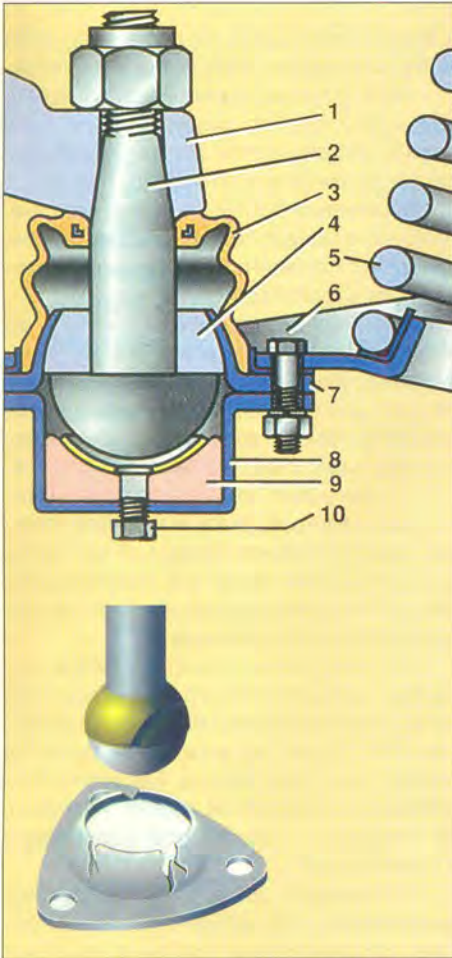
Изношенная нижняя опора: 1 – поворотный кулак; 2 – шаровой палец; 3 – защитный чехол; 4 – подшипник шарового пальца; 5 – пружина; 6 – нижний рычаг; 7 – верхний корпус опоры; 9 – вкладыш; 10 – резиновая пробка.
